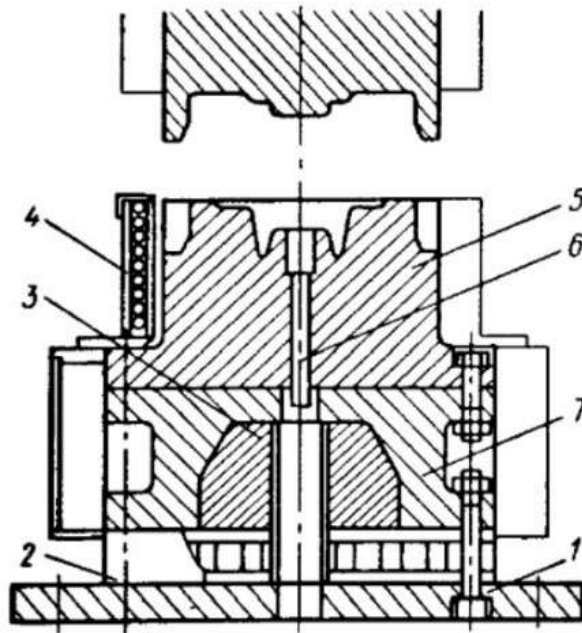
Принципова схема штампу для ізотермічного штампування:
